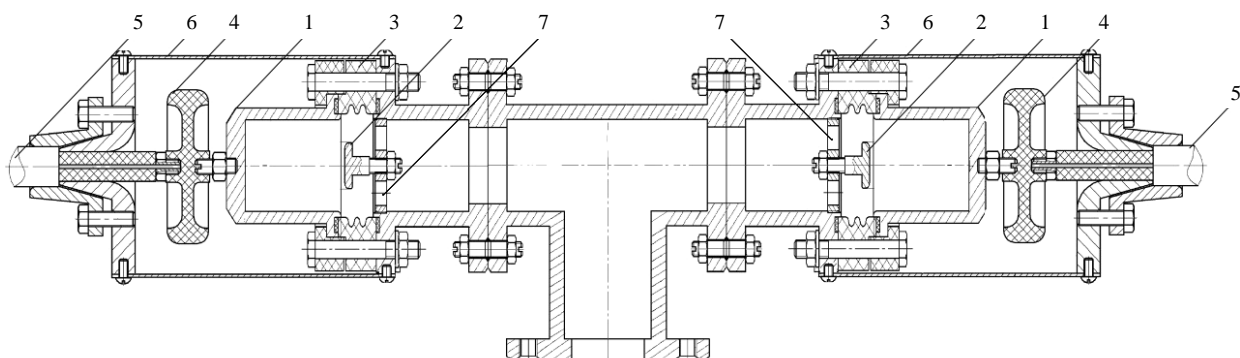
Схема конструкции системы газоразрядных камер с РПК: 1 – полый катод; 2 – анод; 3 – изолятор; 4 – разделительный конденсатор; 5 – фидерная линия; 6 – кожух; 7 – отверстия для откачки
